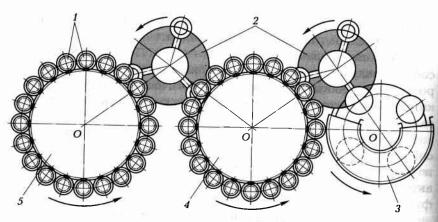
Схема автоматической роторной линии (вид сверху):
